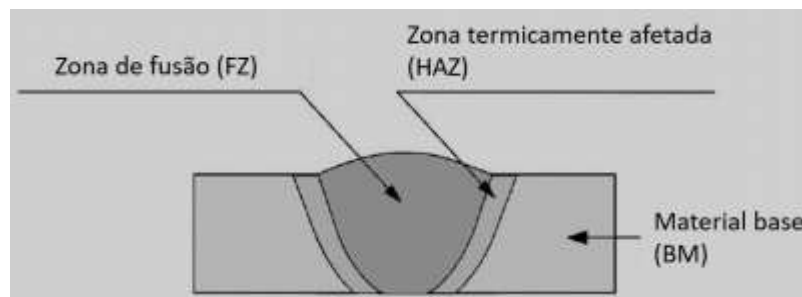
Representação da soldadura e das três zonas do componente
